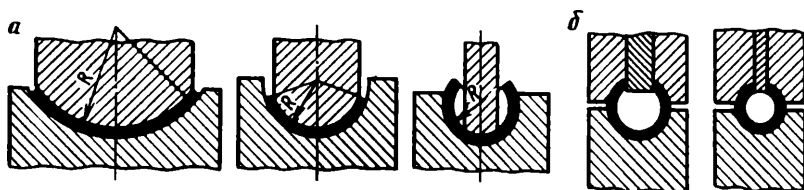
Схема формования прямошовной трубы в открытом (а) и закрытом (б) калибрах валков (R – радиус изгиба заготовки)
